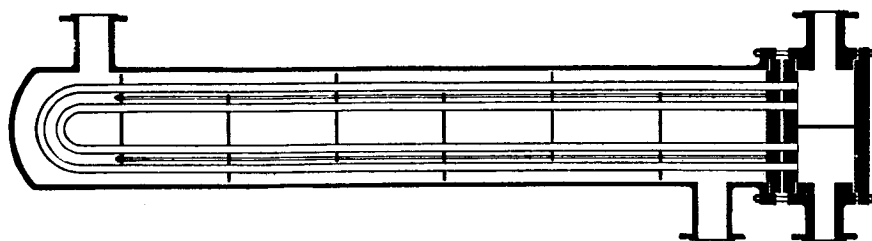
Intercambiador de tubos en U con doble cabezal. (*Patterson Foundry & Machine Co.*)
